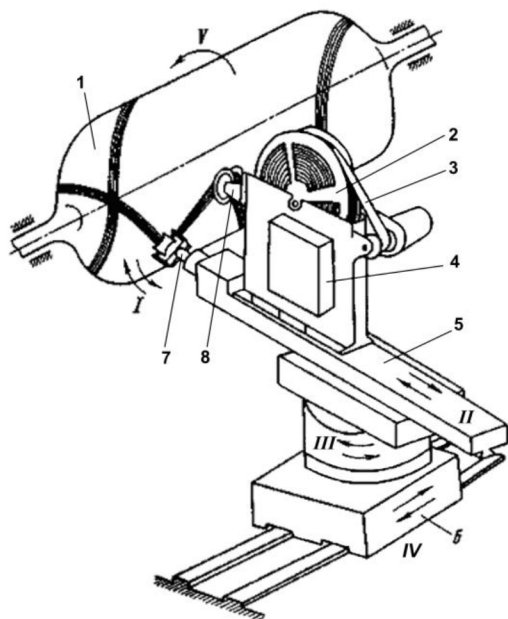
Схема "сухой" намотки препрегом изделия: 1 – оправка; 2 – бобина с препрегом; 3 – разделительная пленка; 4 – нагреватель; 5 – суппорт; 6 – каретка; 7 – головка; 8 - устройство натяжения; I...IV - степени подвижности станка
